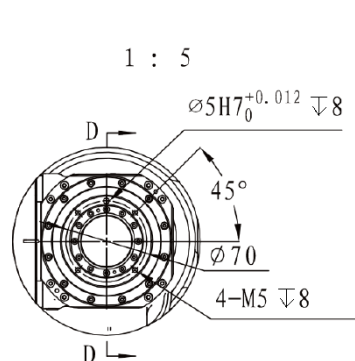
Габаритные чертежи сварочного робота SA10-2000H.
